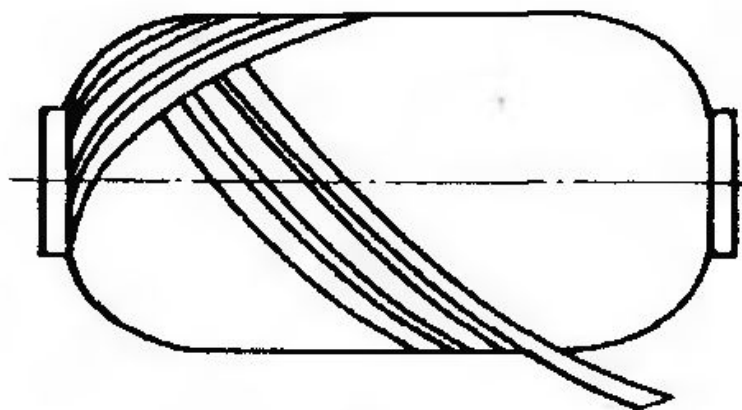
Общий вид оправки для намотки корпуса РДТТ.
